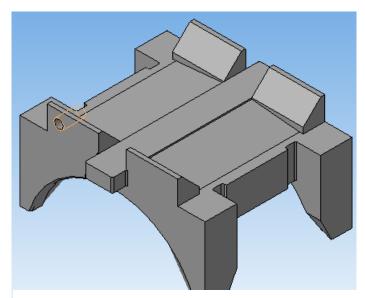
3Д модель "Адаптер подшипникового узла"
